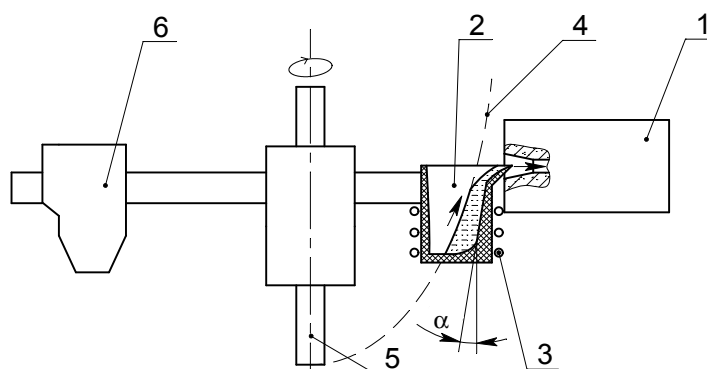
Схема плавильно-заливочного механизма: 1 – литейная форма; 2 – керамический плавильный тигль с расплавом металла; 3 – индуктор; 4 – форма свободной поверхности металла; 5 – ось вращения; 6 – противовес
